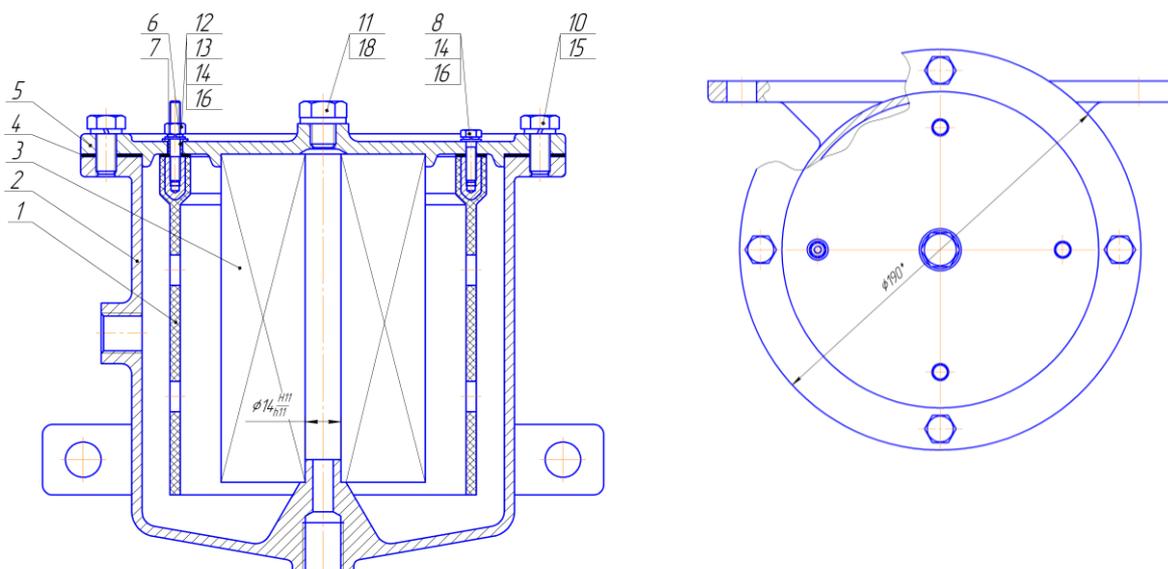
Фильтр тонкой очистки топлива с предпусковым подогревателем топлива из ПТК-керамики:
